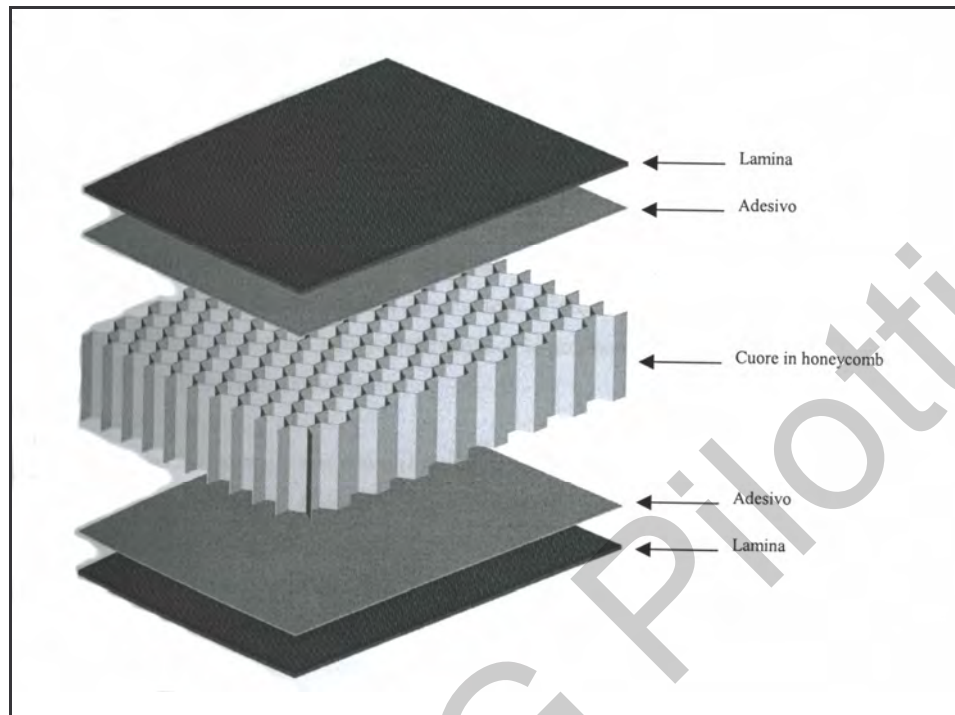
Schema di un pannello sandwich con core in honeycomb
